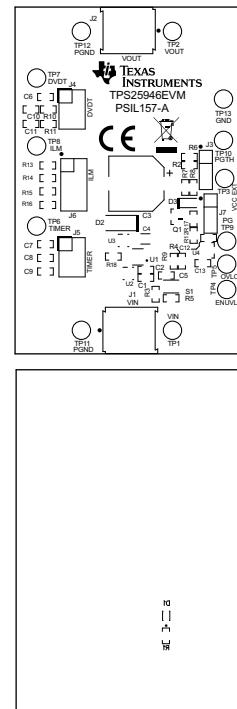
TPS25946EVM 电路板 (a) 顶层装配图 (b) 底层装配图
